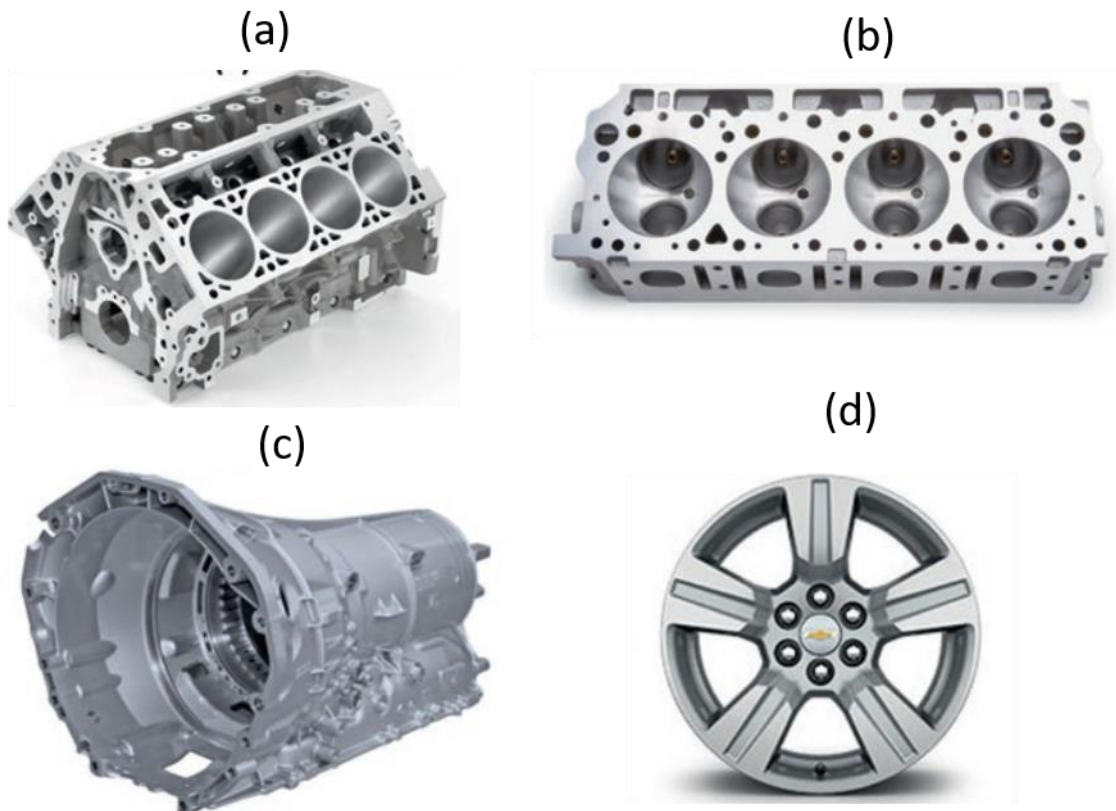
(a)Bloc moteur, procédé de moulage en sable. (b) Culasse, (c)Boîtier de vitesse, (d) Jante de roue[36].
